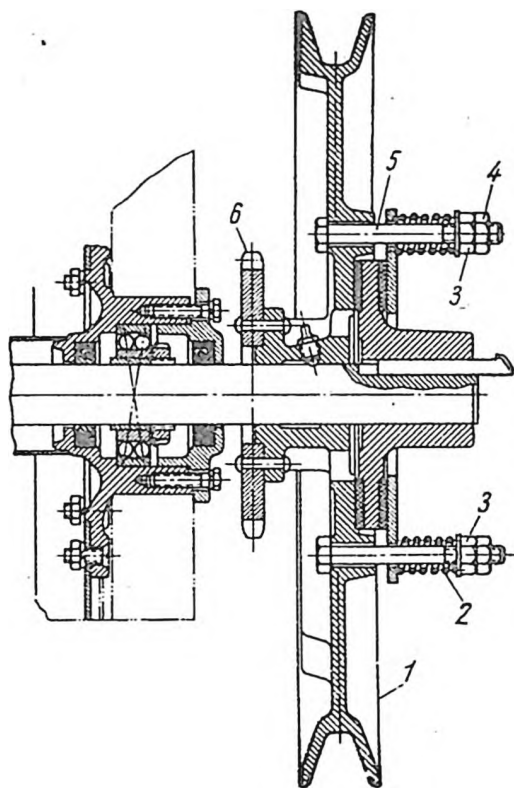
Предохранительная муфта верхнего вала транспортера наклонной камеры: 1 - шкив верхнего вала; 2 - пружина; 4 - контргайка; 6 - звездочка
